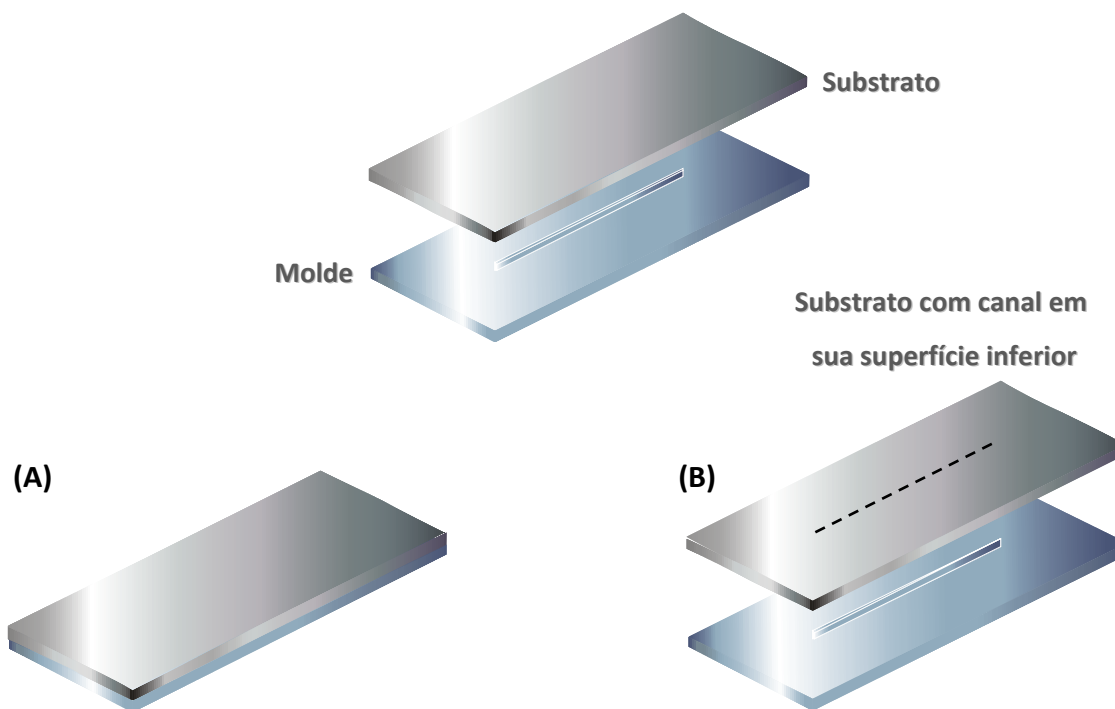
Esquema geral do processo de replicação: (A), moldagem e (B), desmoldagem.
